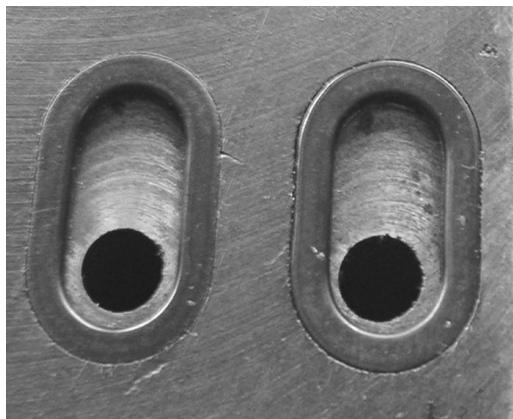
Общий вид контактной поверхности и уплотнителя клапанной крышки гидрораспределителя ГУР 50-3406015А
